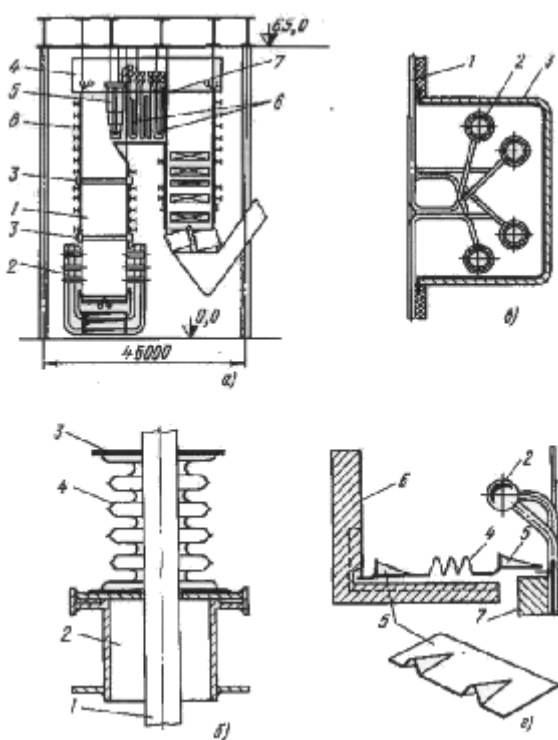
Газоплотный паровой котел и его узлы уплотнения: а - общий вид котла: 1 - топка; 2 - горелки; 3 - узел разъема экранных панелей; 4 - уплотнительный верхний короб (шатер); 5 - ширмовая поверхность пароперегревателя; 6 - конвективная поверхность пароперегревателя; 7 - потолочный экран; 8 - пояс жесткости экранов; б - узел уплотнения прохода труб через стенку: 1 - отводящая труба; 2 - выводная камера; 3 - герметизирующая пластина; 4 - сильфон; в - узел разъема экранных панелей: 1 - газоплотный экран; 2 - смесительный коллектор; 3 - уплотняющий металлический короб с тепловой изоляцией; г - соединение шатра со стеной топки: 1 - газоплотный экран; 2 - коллектор; 3 - подвеска экрана; 4 - сильфонный компенсатор; 5 - гофрированная пластина; 6 - стенка шатра топки; 7 - обмуровка топки.
